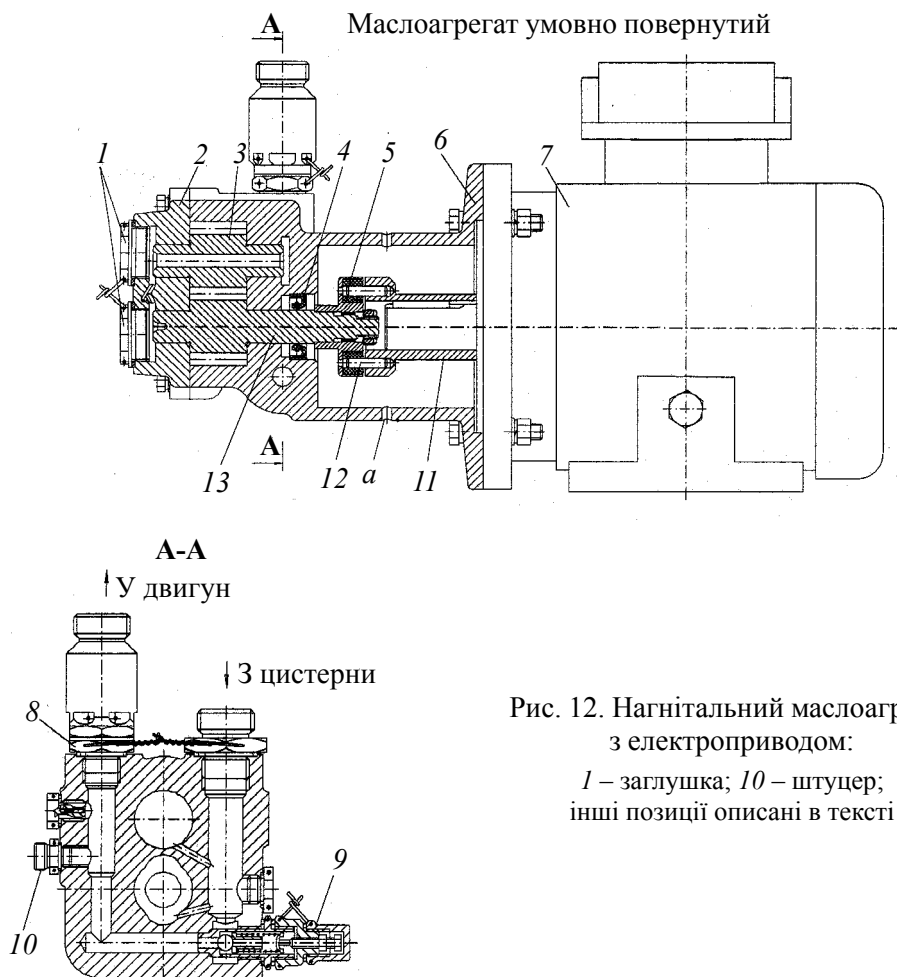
Нагнітальний маслоагрегат з електроприводом:
